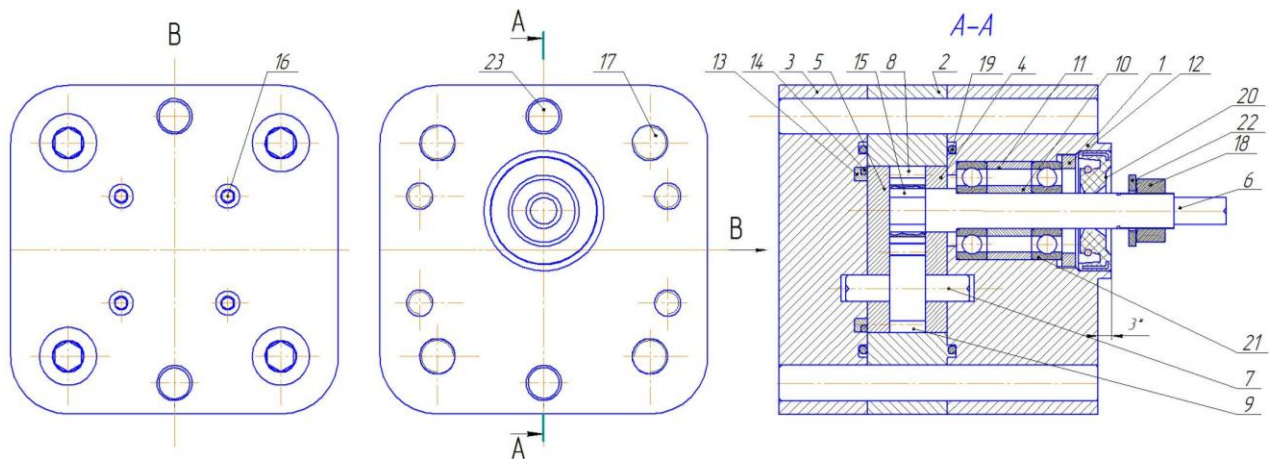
Шестеренный насос с регулируемым торцевым зазором:
